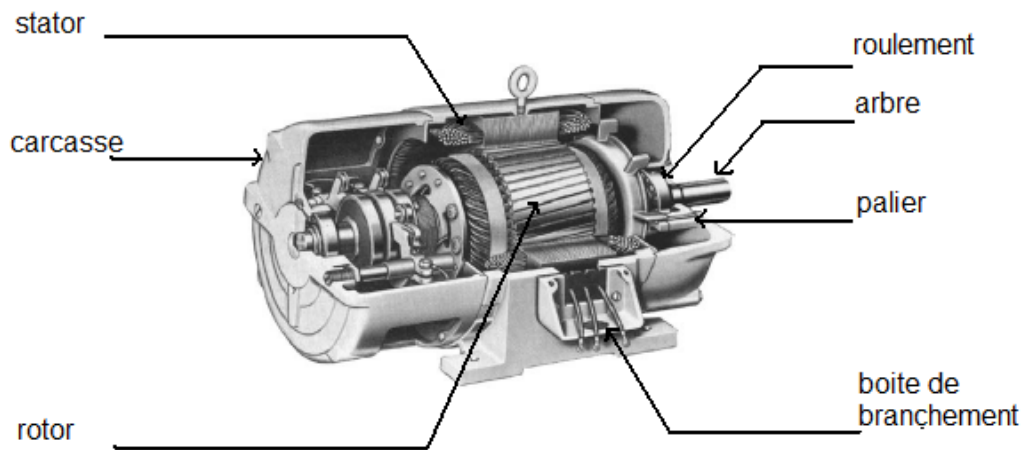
1 – Machine asynchrone à rotor bobiné [3]
